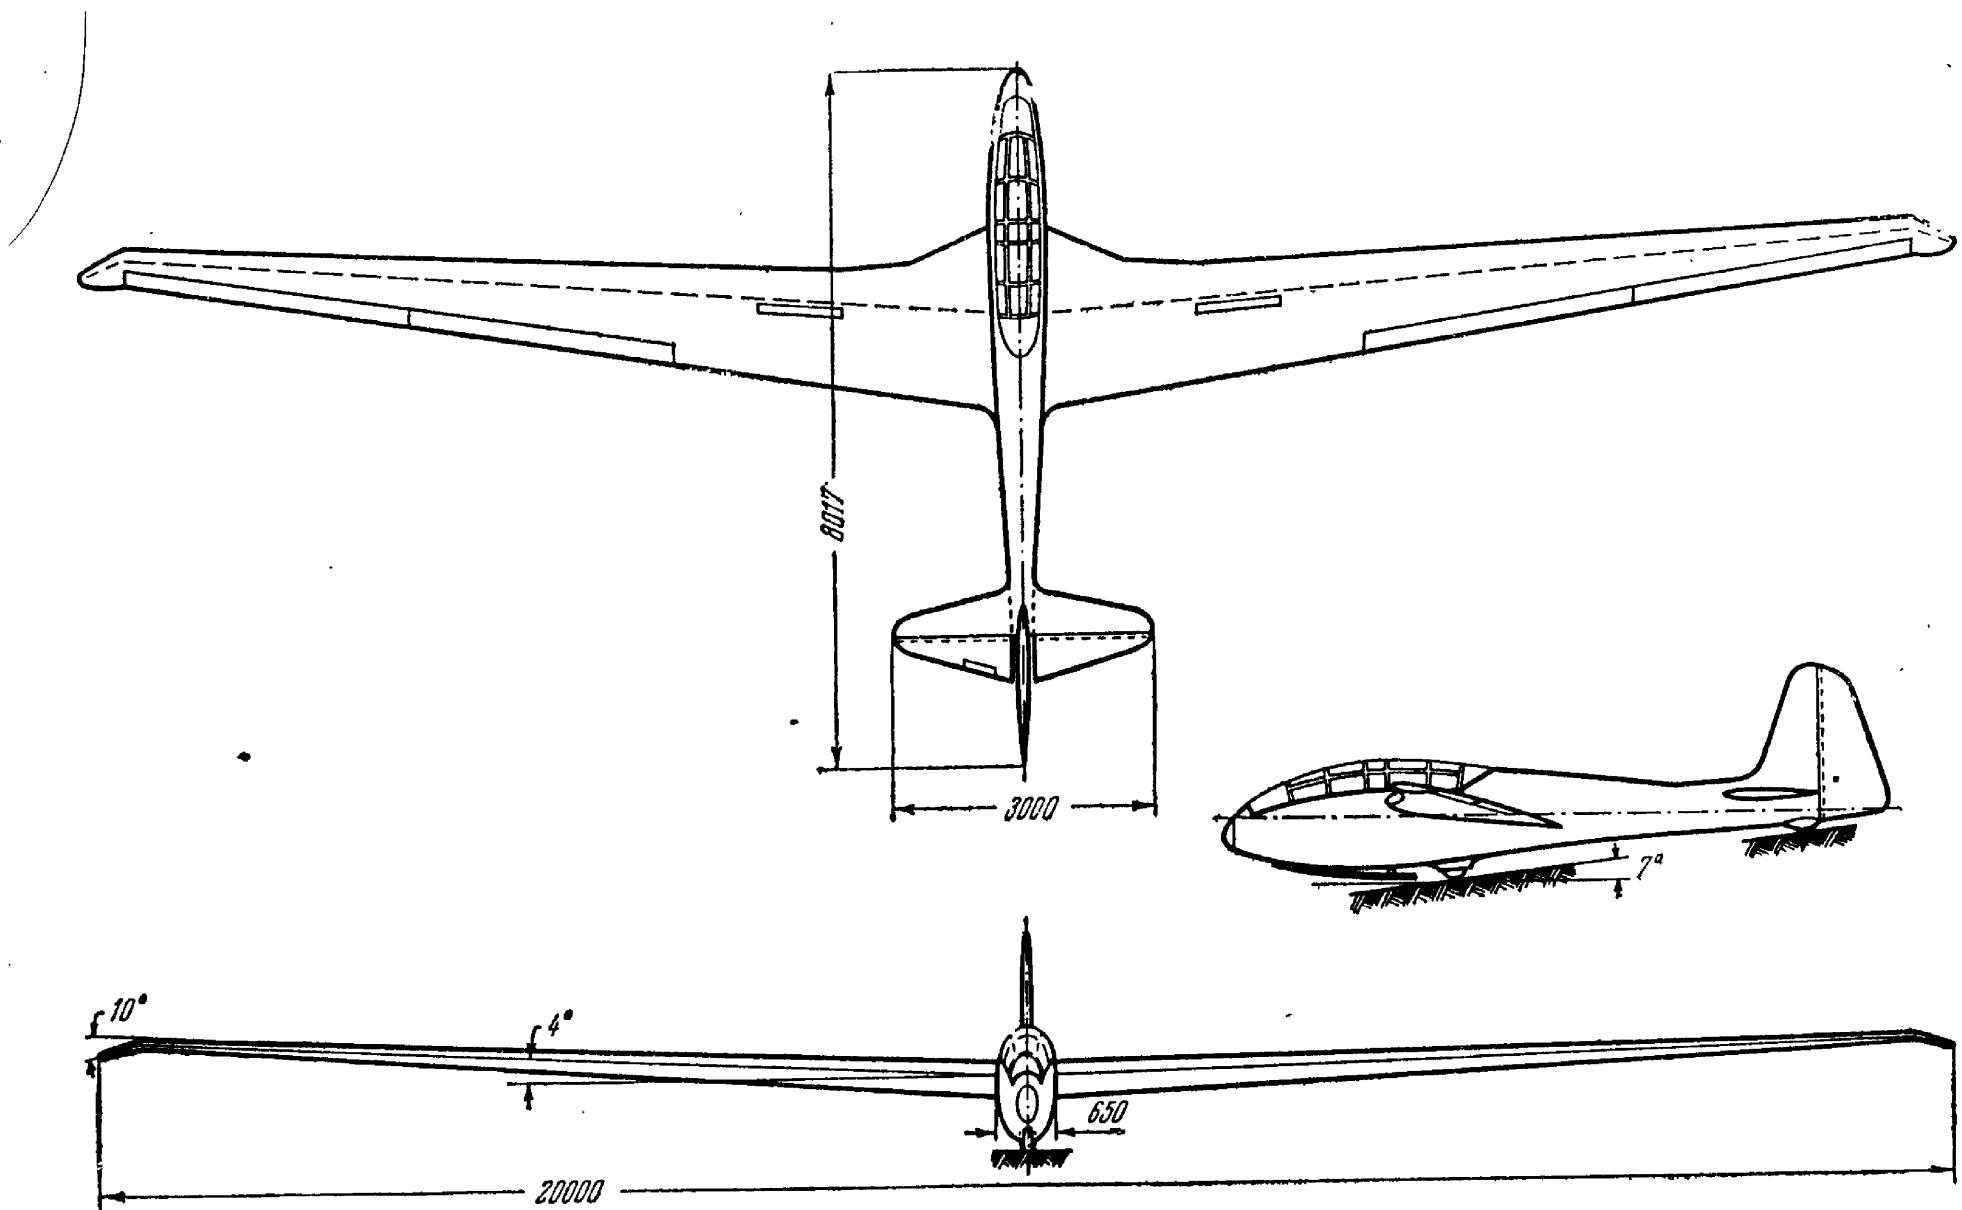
Схема двухместного планера Ш-16 конструкции Б. Н. Шереметева
